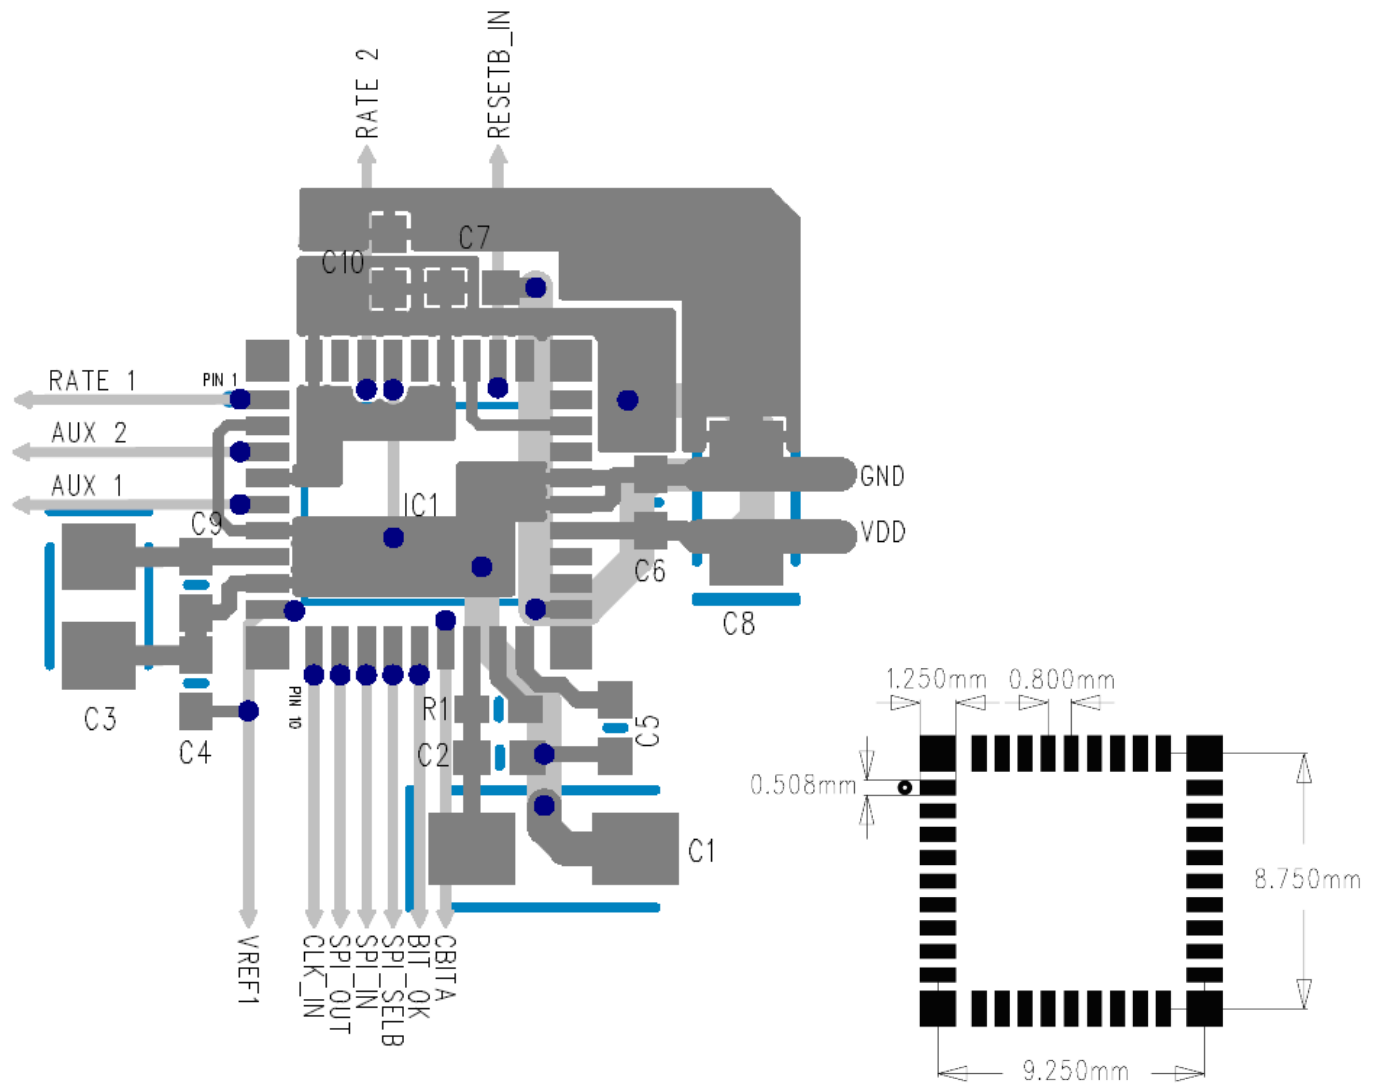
推奨レイアウト / Recommended PCB layout
